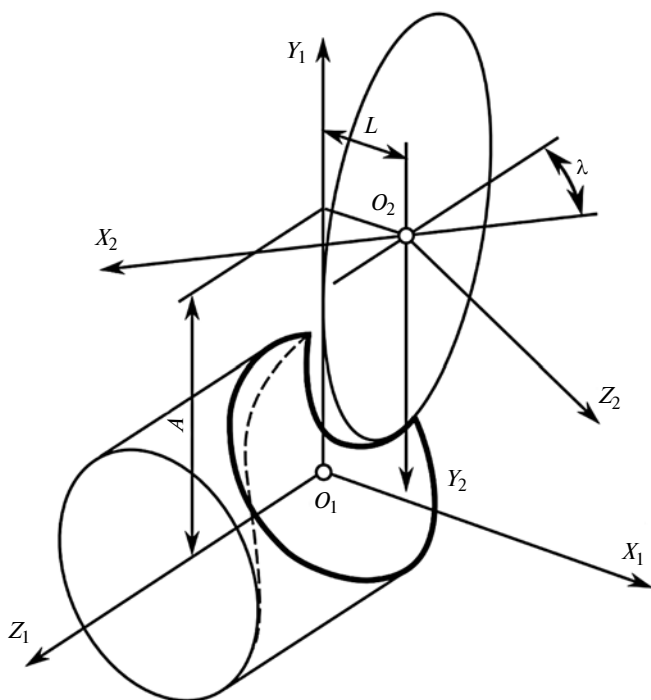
Координатная схема расчета профиля дисковой фрезы
